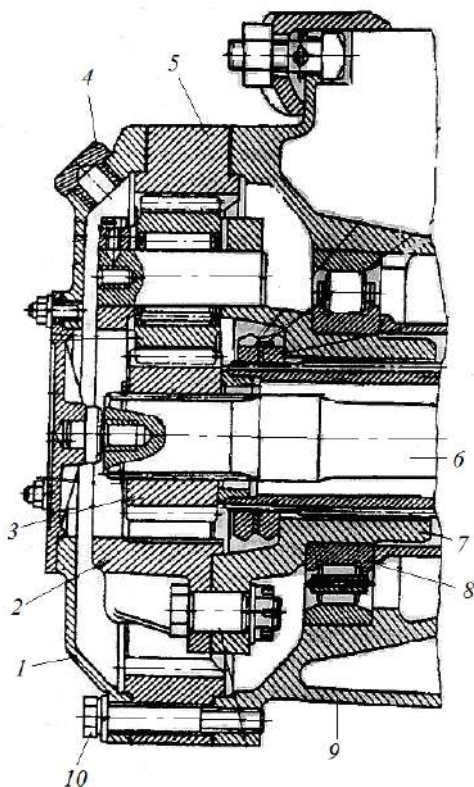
Бортовий редуктор із зовнішнім зачепленням:
